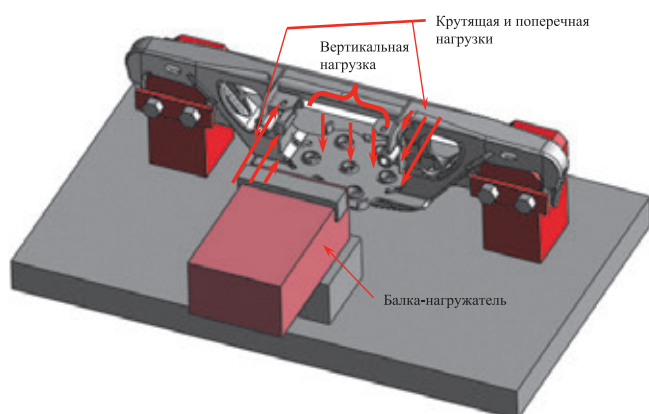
Схема уточненных стендовых усталостных испытаний
